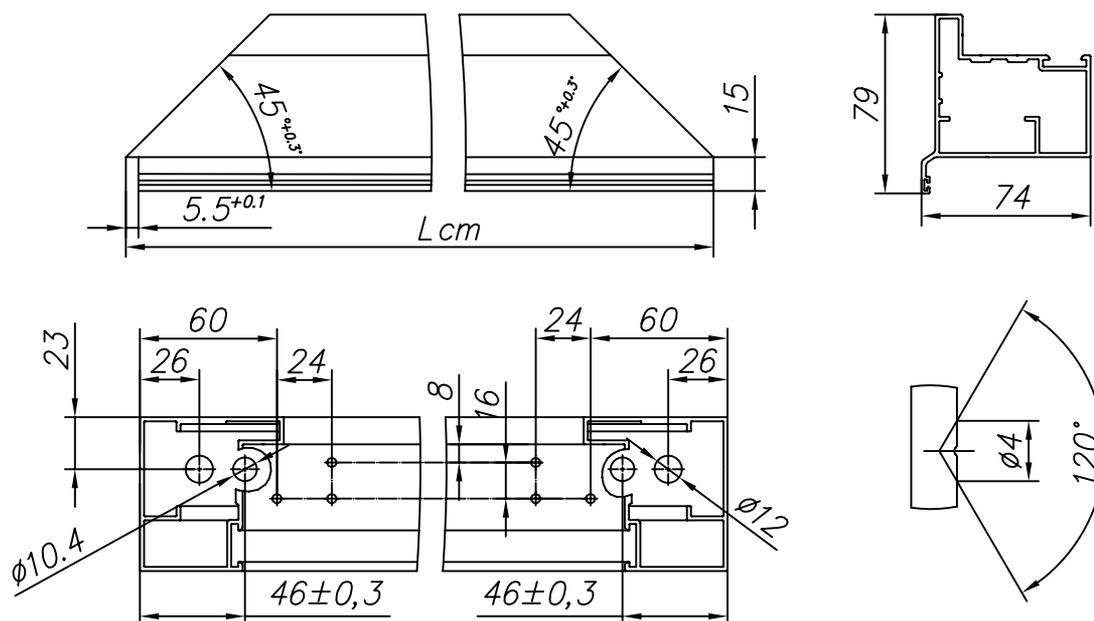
Изготовление стойки (профиль рамы FLGU.400.0111)
